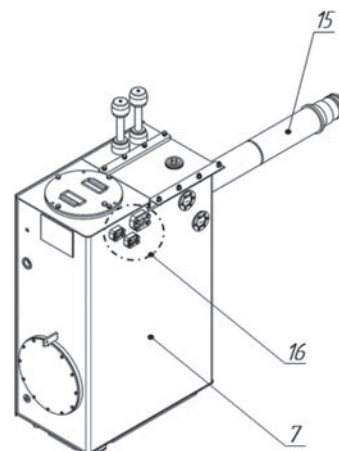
Модернизированный стандартный масляный бак: 7 – модернизированный стандартный масляный бак; 15 – всасывающий патрубок; 16 – каналы слива рабочей жидкости /
